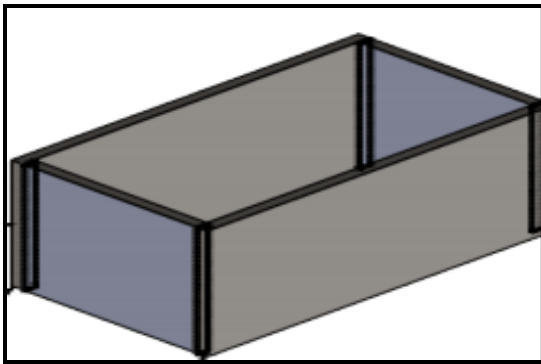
Indicación de soldadura de la pieza MBC-C-13-3.
